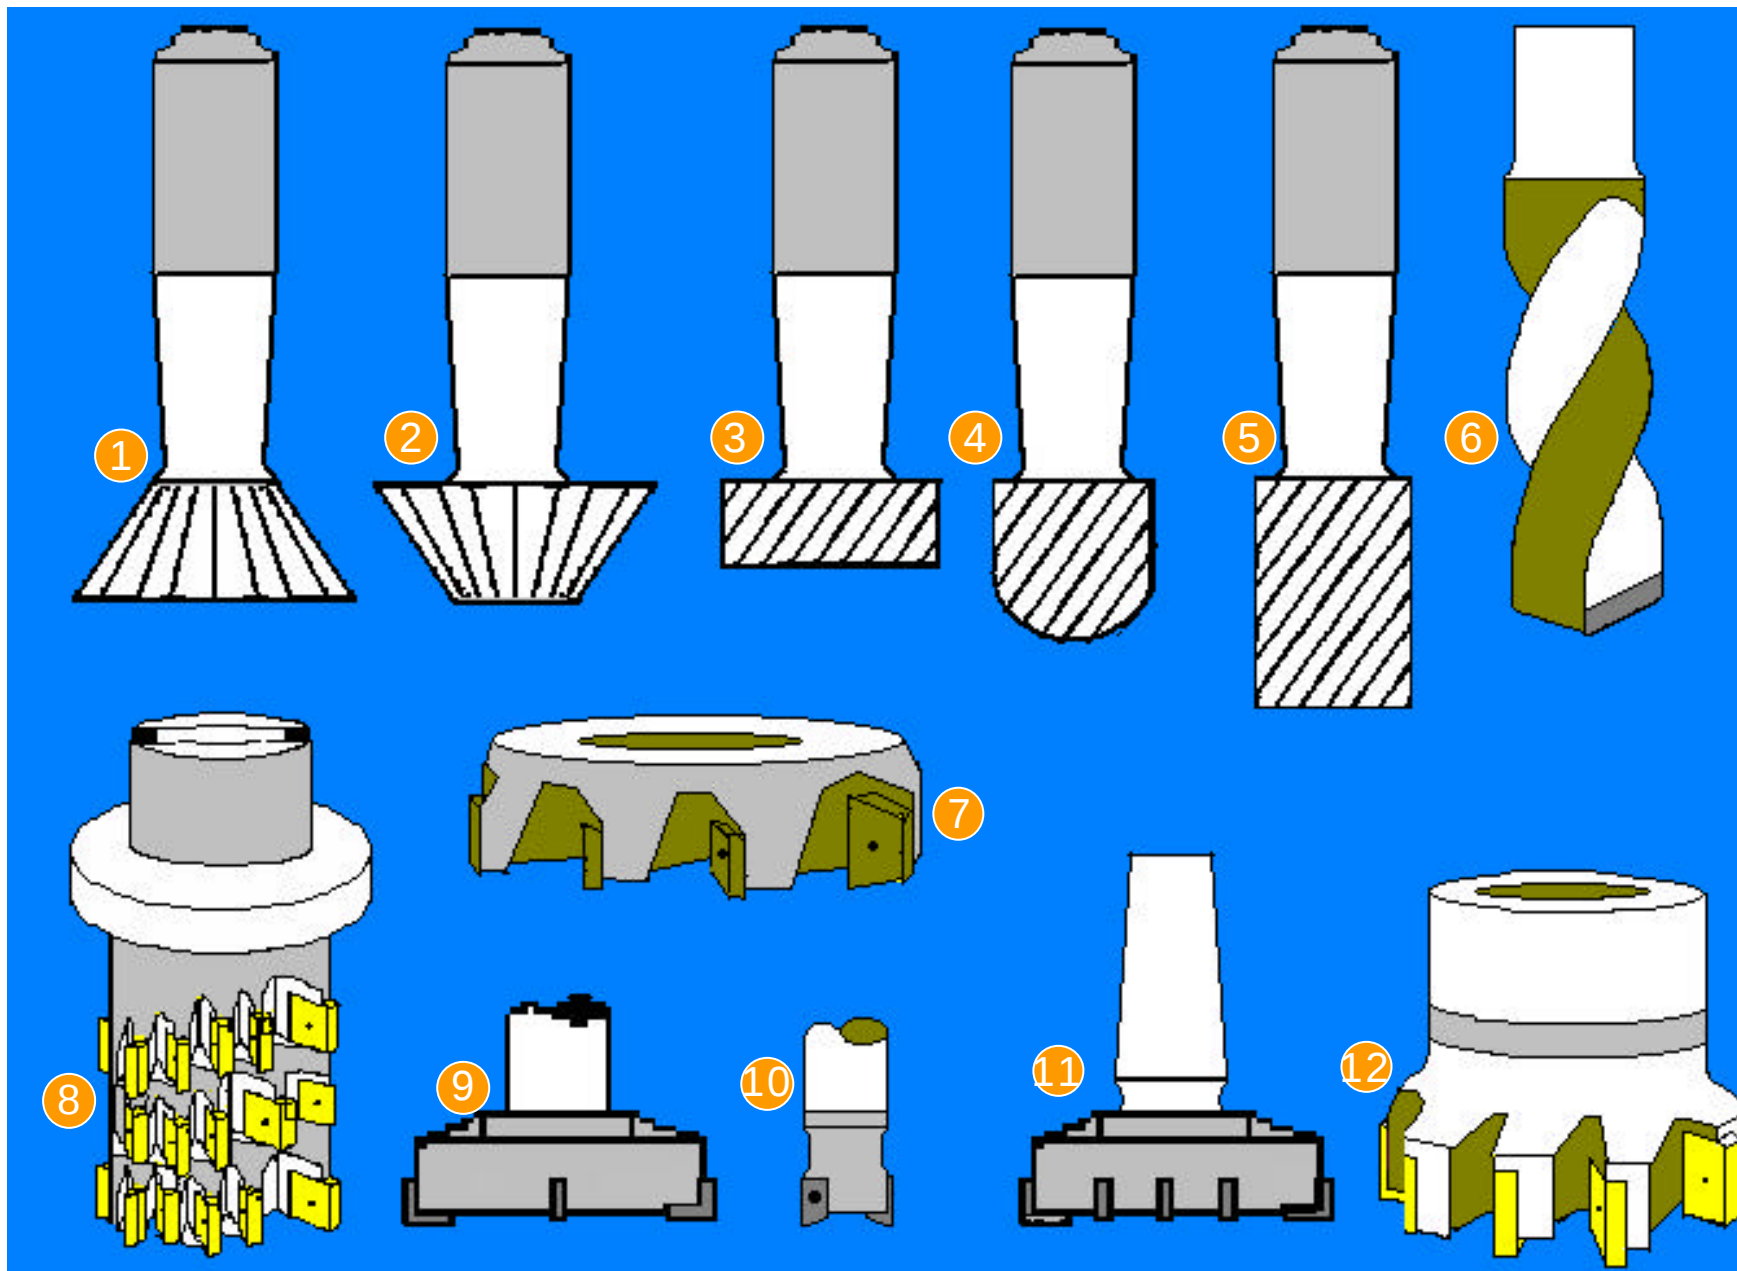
Ferramentas para usinagem das peças apresentadas neste trabalho
